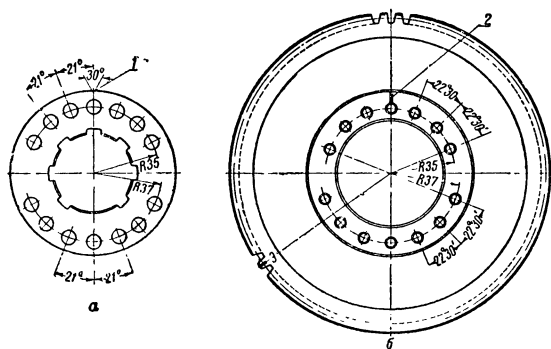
Детали привода топливного насоса: а — шлицевой фланец; б — шестерня привода; 1 и 2 — метки.
